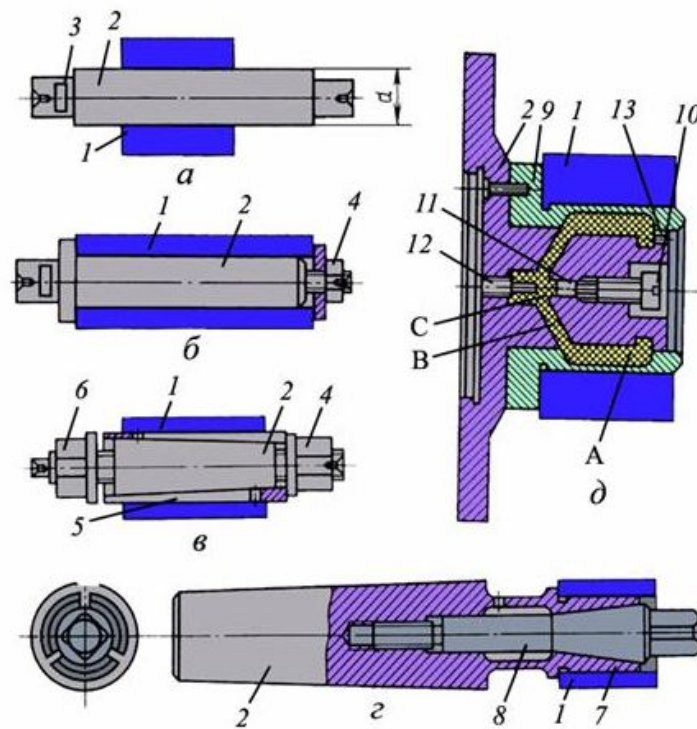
Токарні оправки (а, б, в, г, д): 1 – заготовка 2 – оправка 3 – лиска 4,6 – гайка 5 – цанга 7 – циліндрична поверхня 8 – болт 9 – втулка 10 – гвинт 11 – плунжер 12 – упор 13 - пробка
